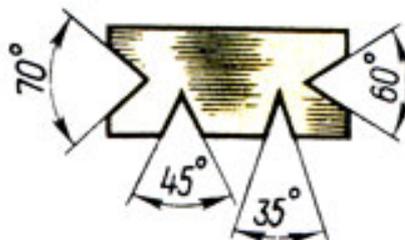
Шаблон для проверки угла заточки зубила
